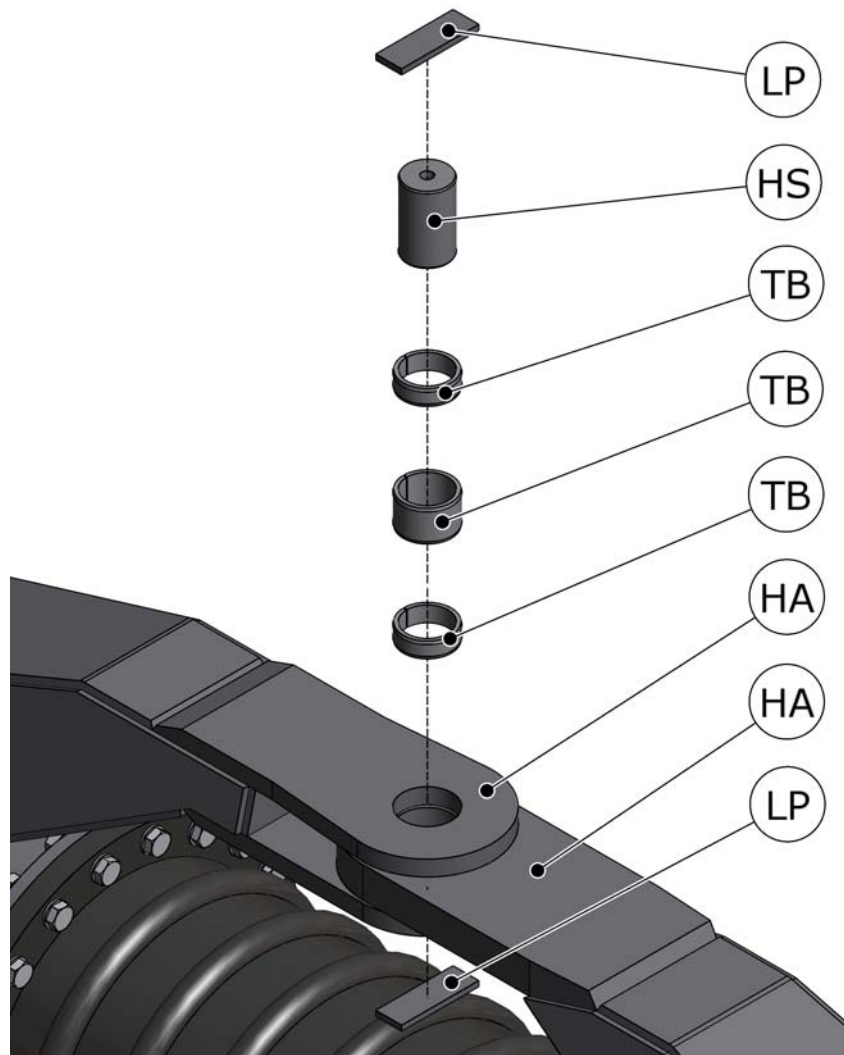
Remplacement des bagues de serrage du joint cardan / simple
